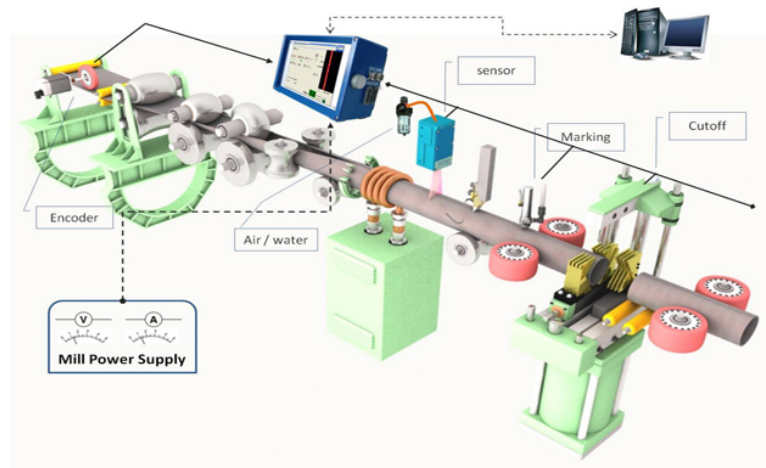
Equipamento de conformação de tubo e respetiva soldadura por resistência ERW [60]
